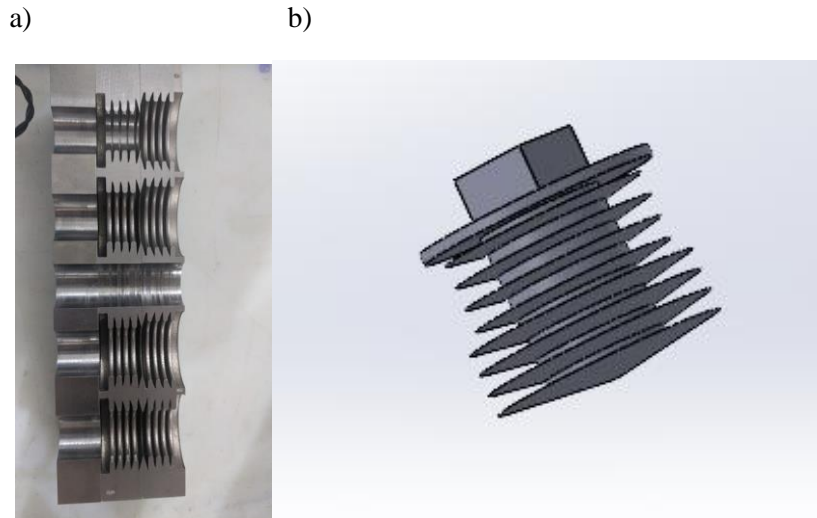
a) Inserto para molde de inyección fabricado mediante erosión por penetración.
